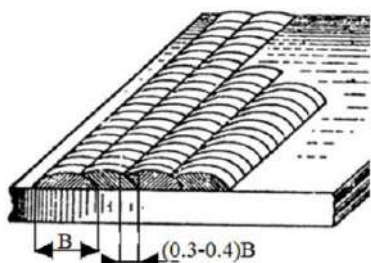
Наплавка металла на плоский лист узкими валиками с перекрытием
